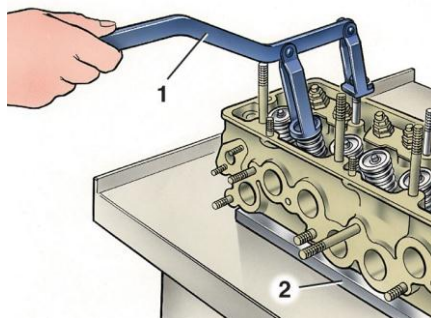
Снятие и установка клапанных пружин приспособлением: 1 – приспособление А.60311/R; 2 – монтажная доска А.60335
